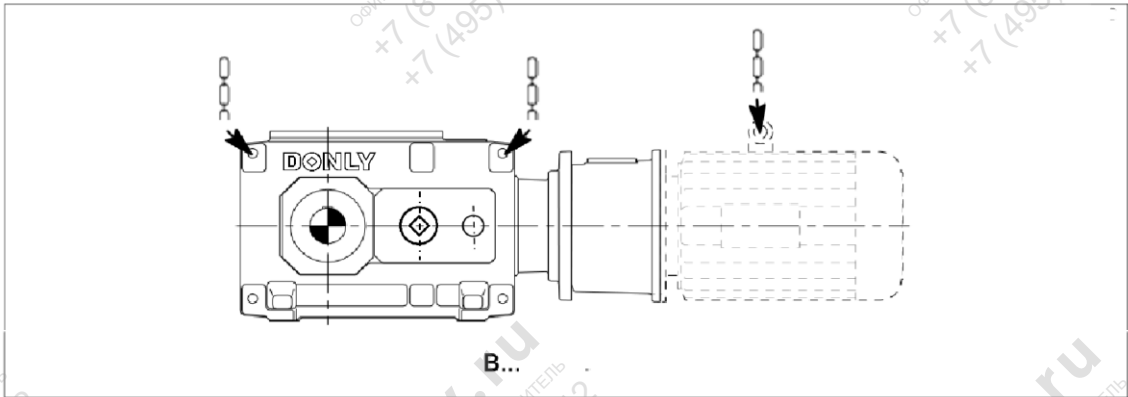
Расположение точек крепления на редукторах модели DLB с поворотным основанием редуктора
